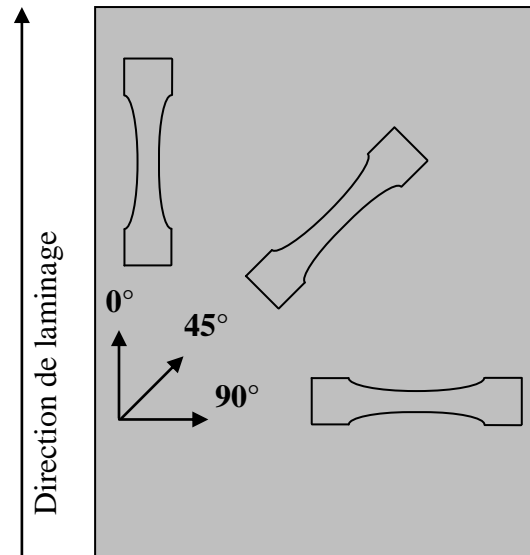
Sens de prélèvement des éprouvettes par rapport à la direction de laminage.
